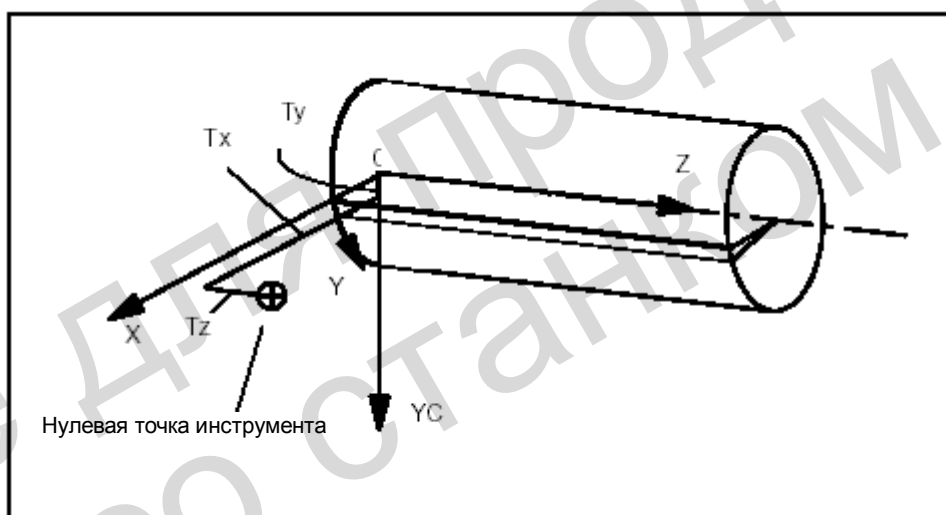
Положение нулевой точки инструмента к нулевой точке станка
